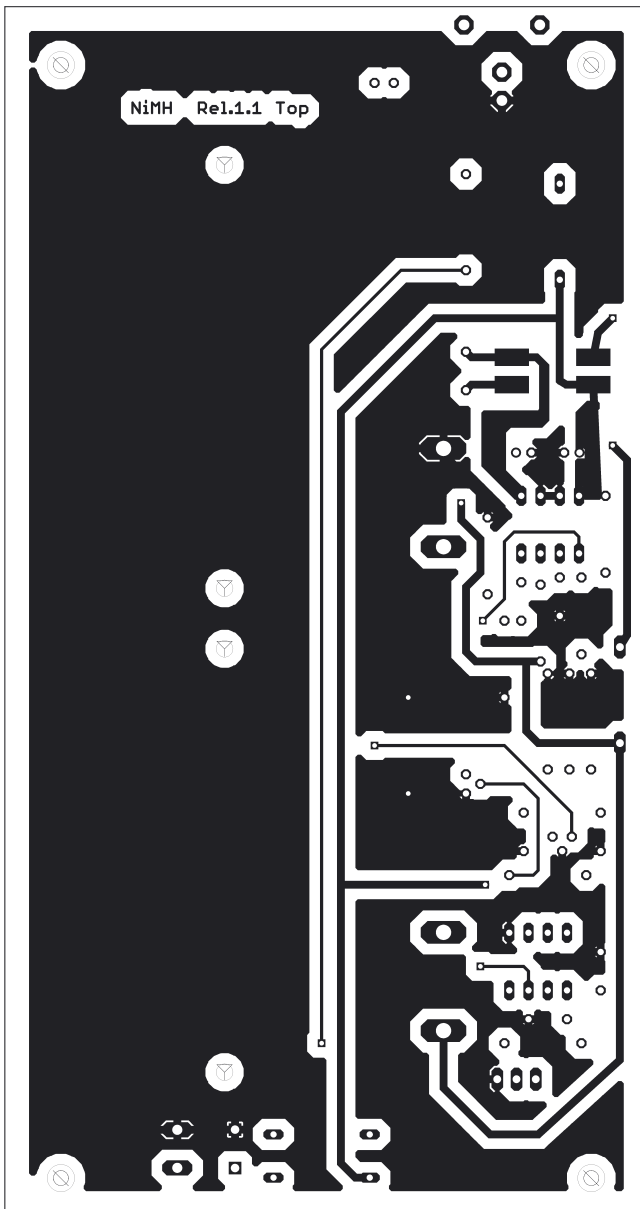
Layout der Bestückungsseite der Ladebaugruppe
